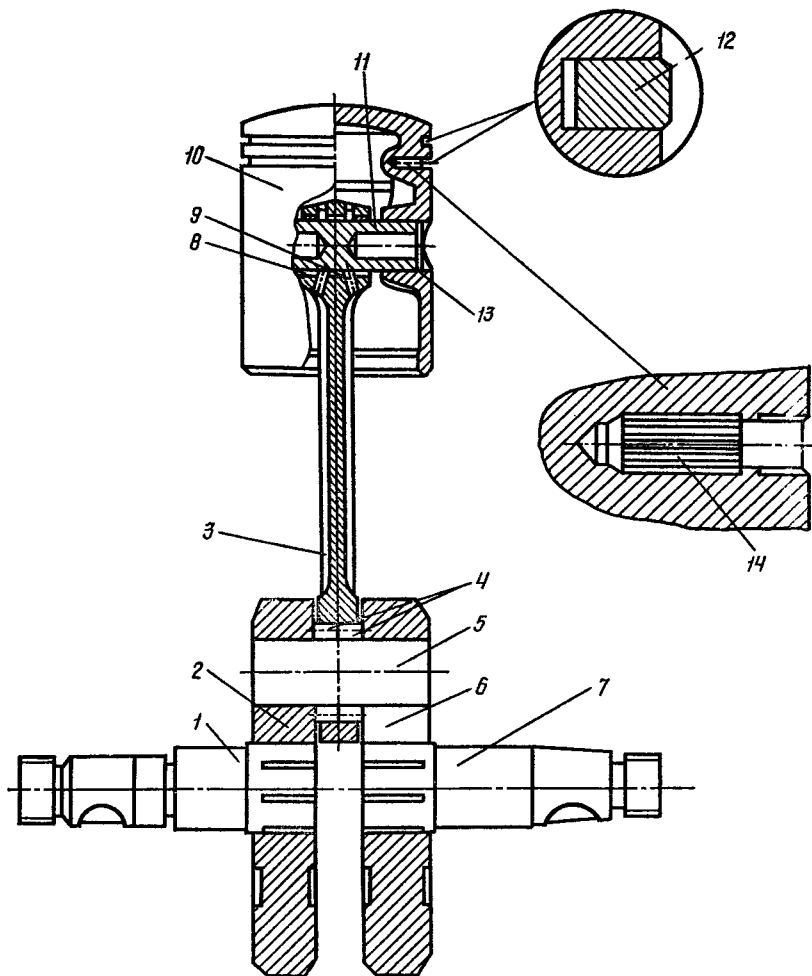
Коленчатый вал в сборе с шатуном и поршнем:
